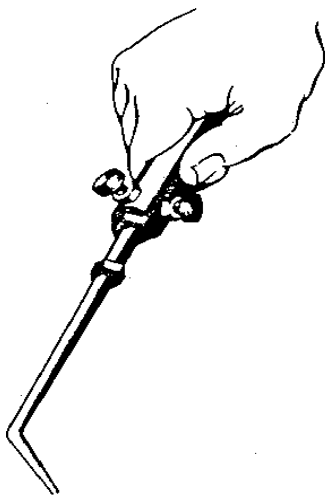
Posição do maçarico para soldar metais pesados com acetileno.
